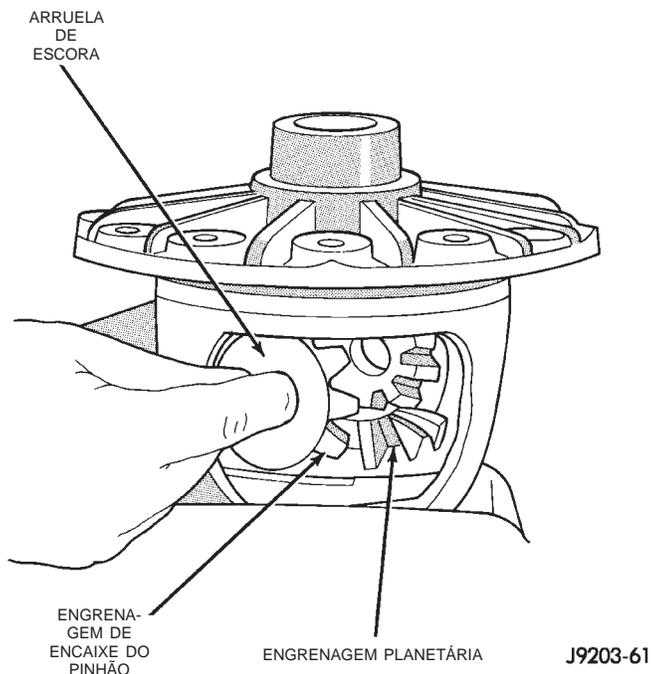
Remoção da Engrenagem de Encaixe do Pinhão
